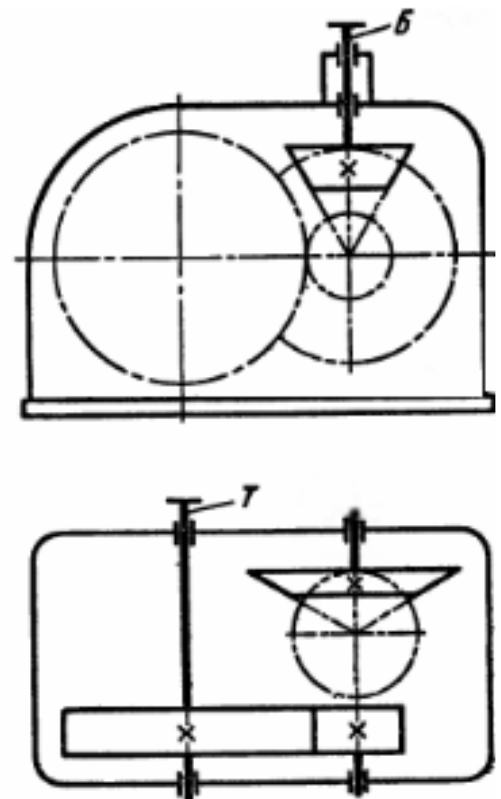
Коническо-цилиндрический двухступенчатый редуктор с вертикальным тихоходным валом:
